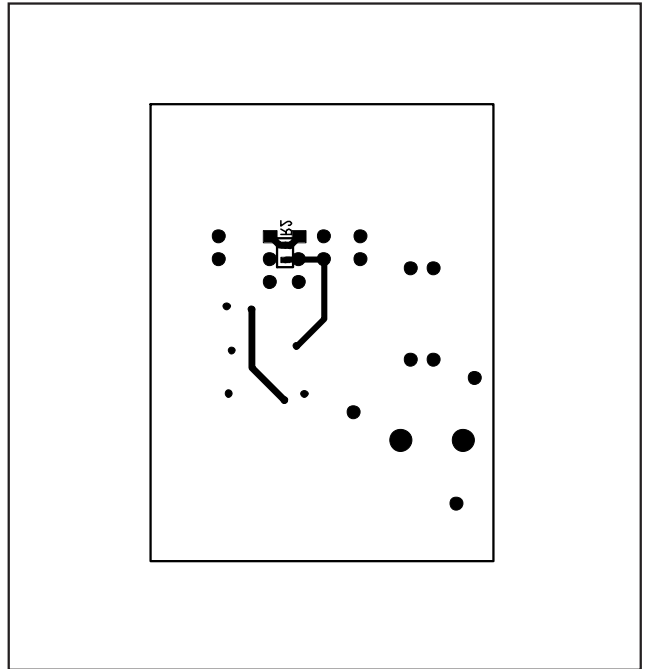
MAX4411 评估板元件布局 — 焊接层
